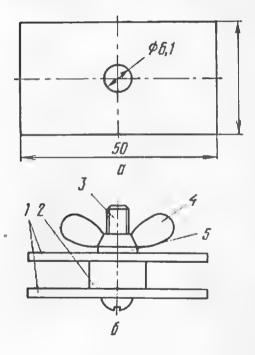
1 — щечка [дюралюминий толщиной 1...2 мм], 2 шт.; 2 — бобышка; 3 — винт M6×20; 4 — барашек [гайка] M6; 5 — шайба
